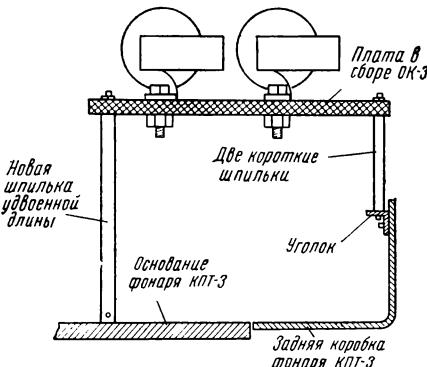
Предлагаемый способ установки платы в сборе ОК-3
